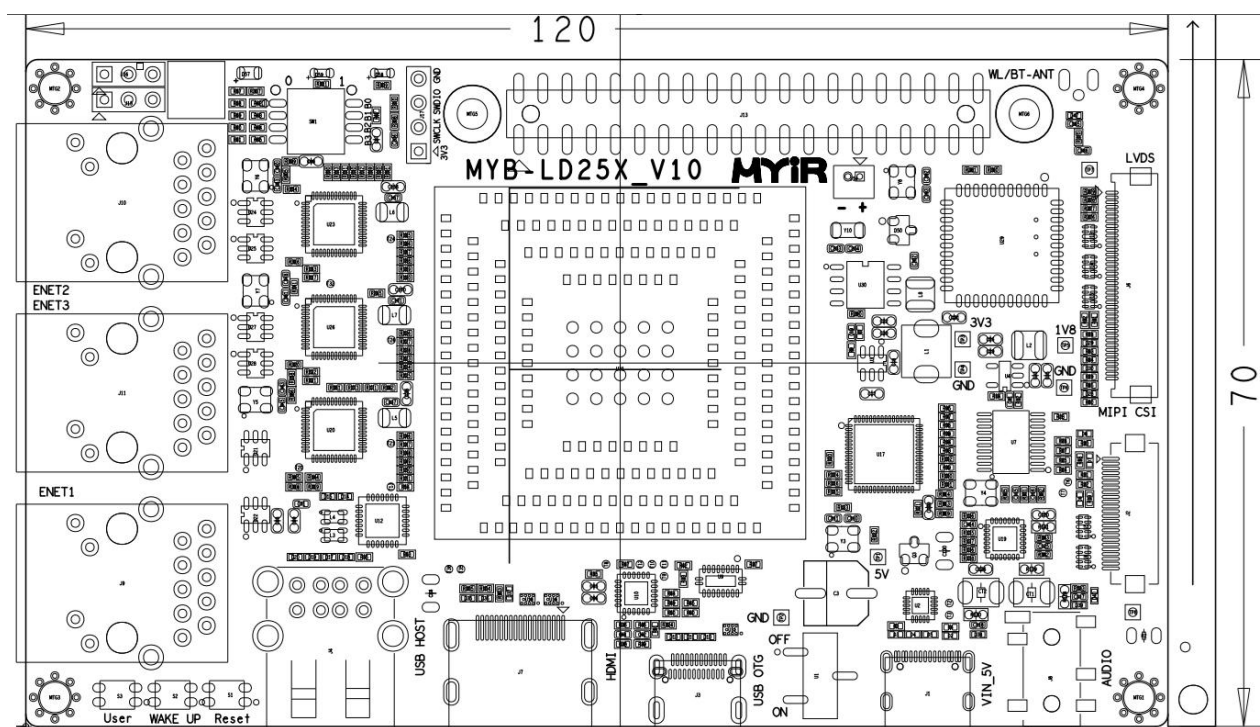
2 MYD-LD25X 评估板尺寸 (mm)
